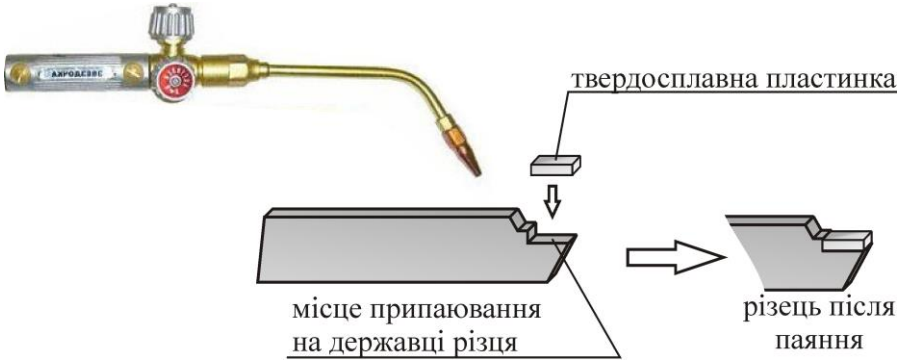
Технологічна схема припаювання твердосплавної ріжучої пластини до державки токарного різця
